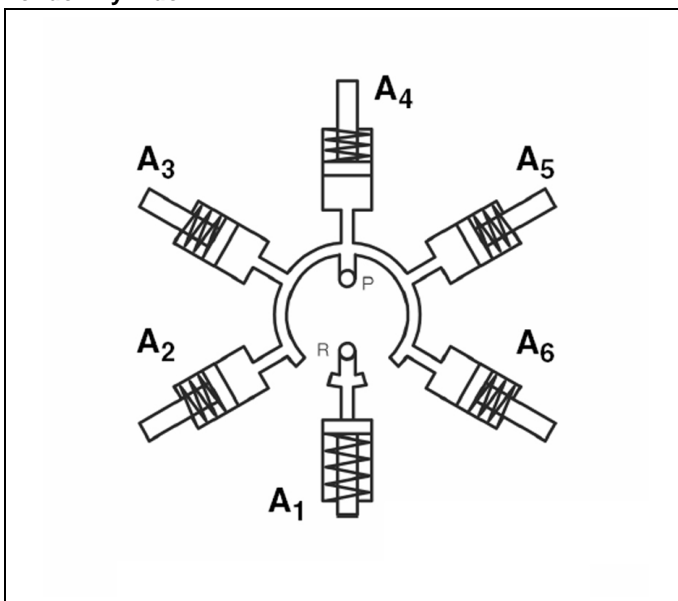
Beispiel für gesteuerte Drehdurchführung mit einfach wirkenden Zylindern
